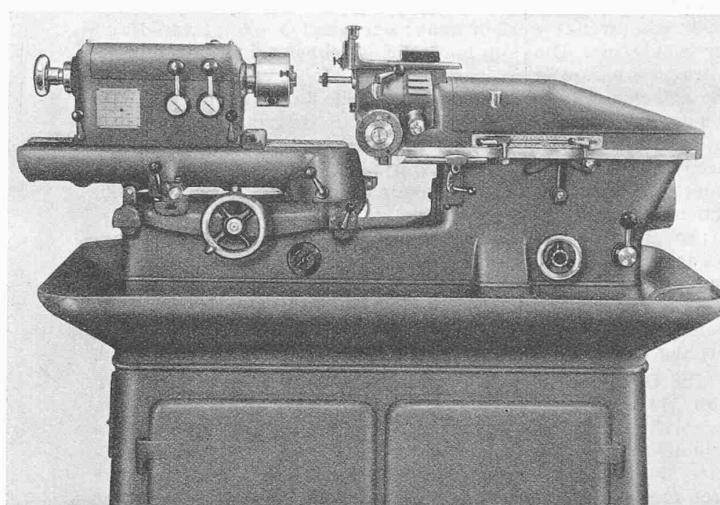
Innenschleifmaschine «Voumard» der Schweiz. Werkzeugmaschinenfabrik
